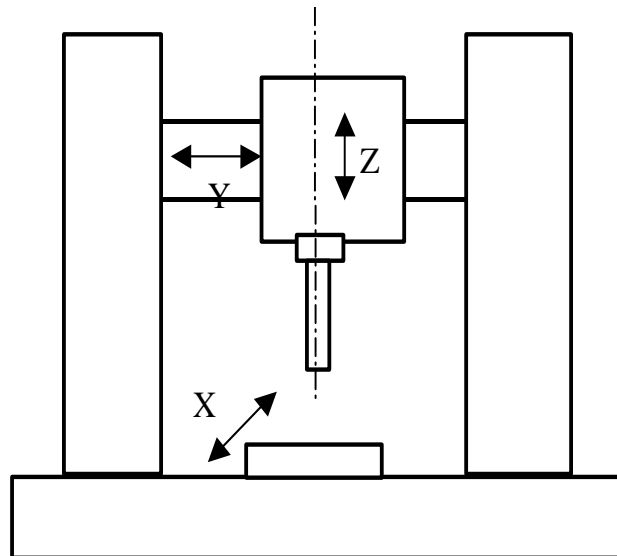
Компонування поздовжньо-фрезерного верстата
